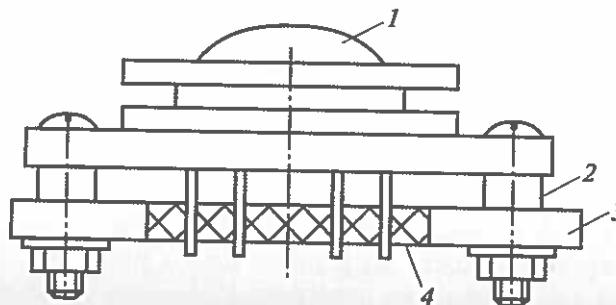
Установка ИМС со штыревыми выводами на печатной плате с дополнительным механическим креплением:
